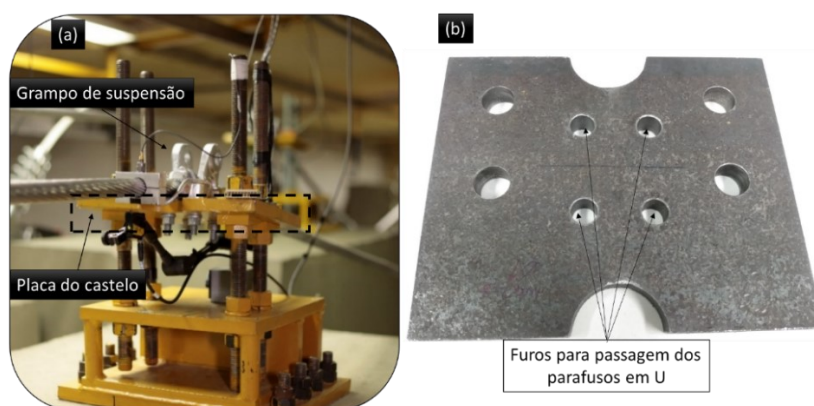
(a) Castelo utilizado na montagem do grampo de suspensão metálico ao cabo condutor; (b) Placa do castelo
